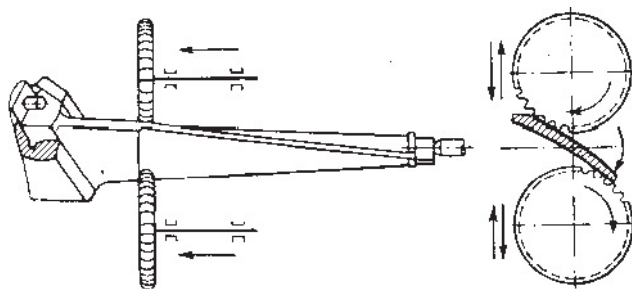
Схема одночасного фрезерування корита і спинки пера лопатки вузькими поперечними строчками.
